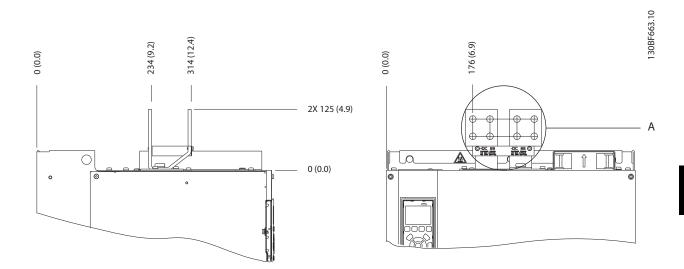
Dimensions des bornes de secteur, moteur et terre E3h (vues latérales)
